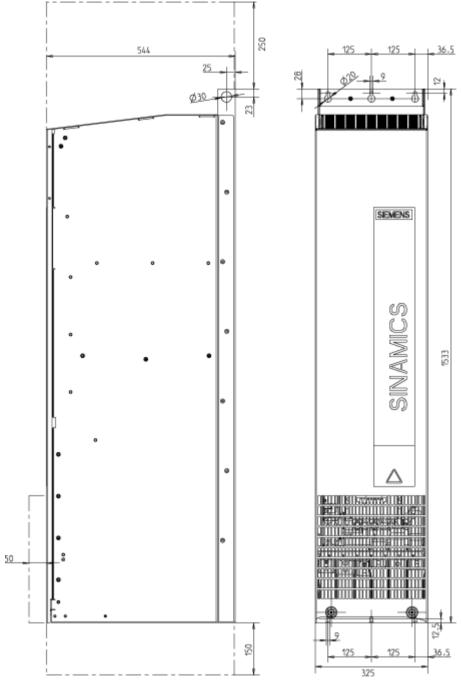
Габаритный чертеж активного интерфейсного модуля, типоразмер GI. Вид сбоку, вид спереди
